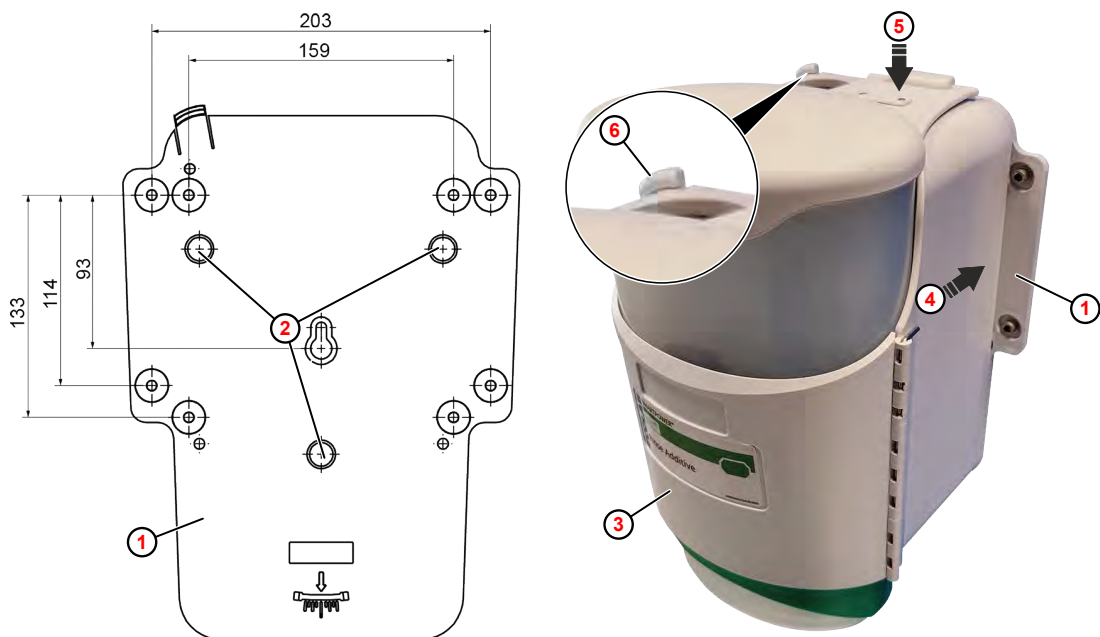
Gerät montieren (Beispiel Rinse Dispenser)
